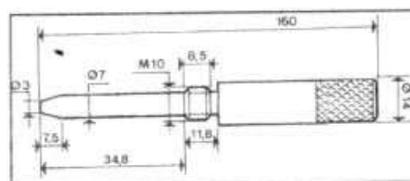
E.12. Размеры оправки для установки коленчатого вала в положение ВМТ.
